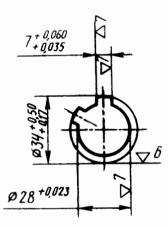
Чертеж для проверки возможности сцепления сменных шестерен на станках 16К20, 16К20Г
